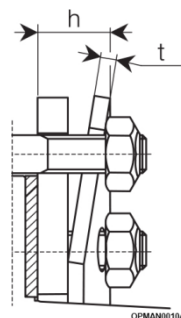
Guide de dimension pour réglage d'embrayage
